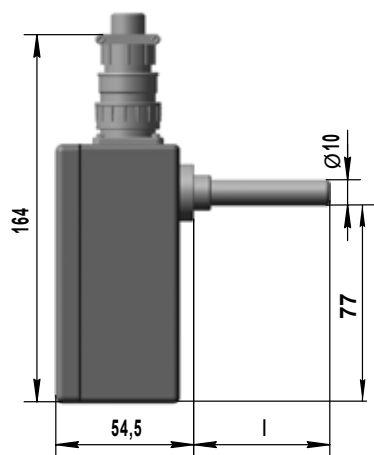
Материал корпуса - стеклонаполненный полиамид
